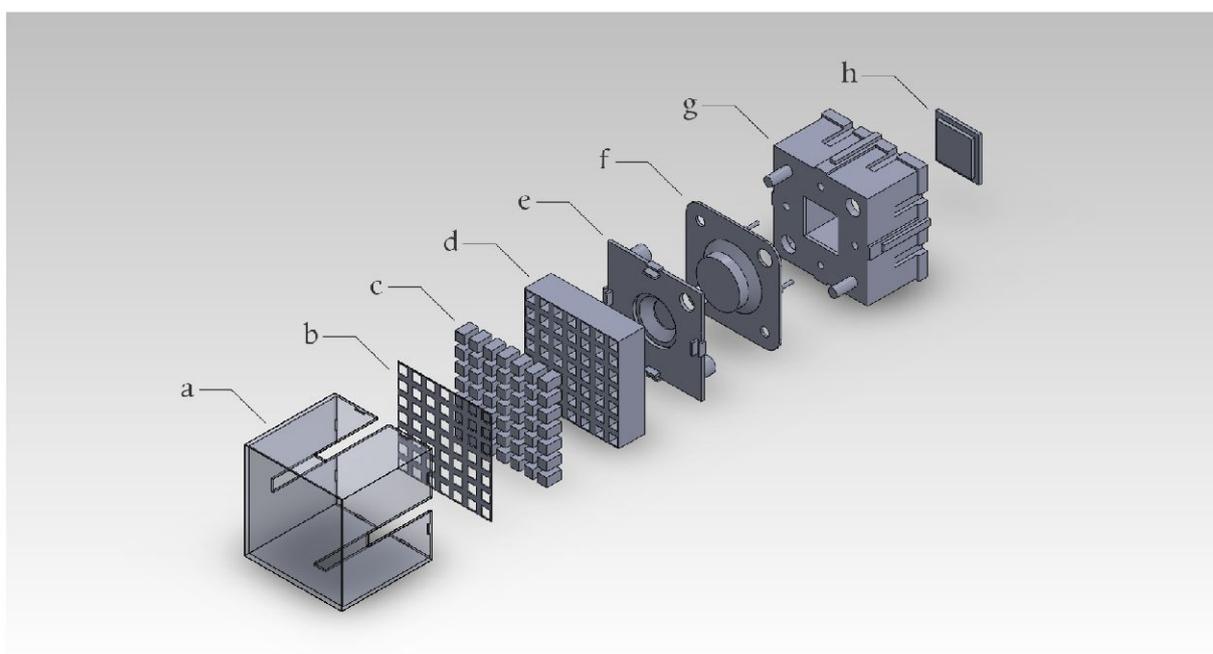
Botão LED do CHU 2836. Perspectiva explodida.
